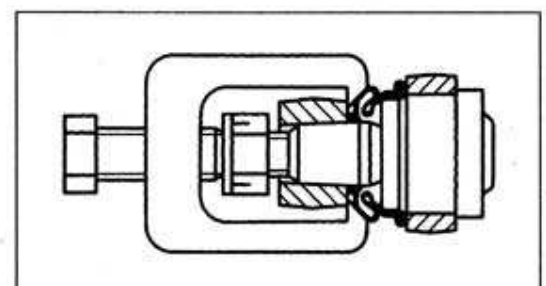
Выпрессовка пальца шарнира рулевых тяг универсальным съемником
